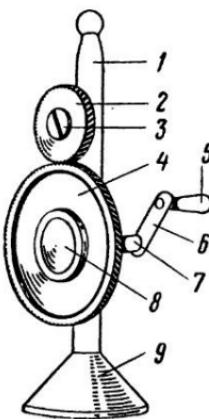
Модель передачи зубчатыми колесами с косым зубом: 1 — стойка; 2 — ведомое колесо; 3 — ось ведомого колеса; 4 — ведущее колесо; 5 — ручка; 6 — рычаг ручки; 7 — упорная втулка; 8 — вал привода; 9 — основание.
